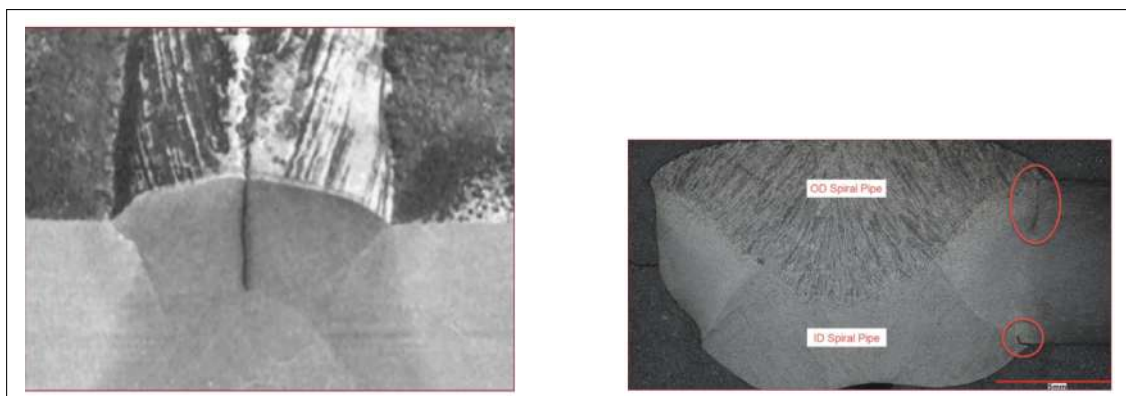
Fissure dans des joints soudés [21]
